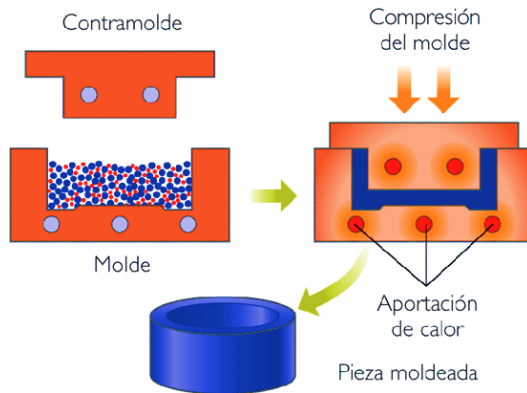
Sintetización de piezas de plástico mediante moldeo por compresión. 1) Carga del compuesto en el molde 2) Compresión y calentamiento del material
